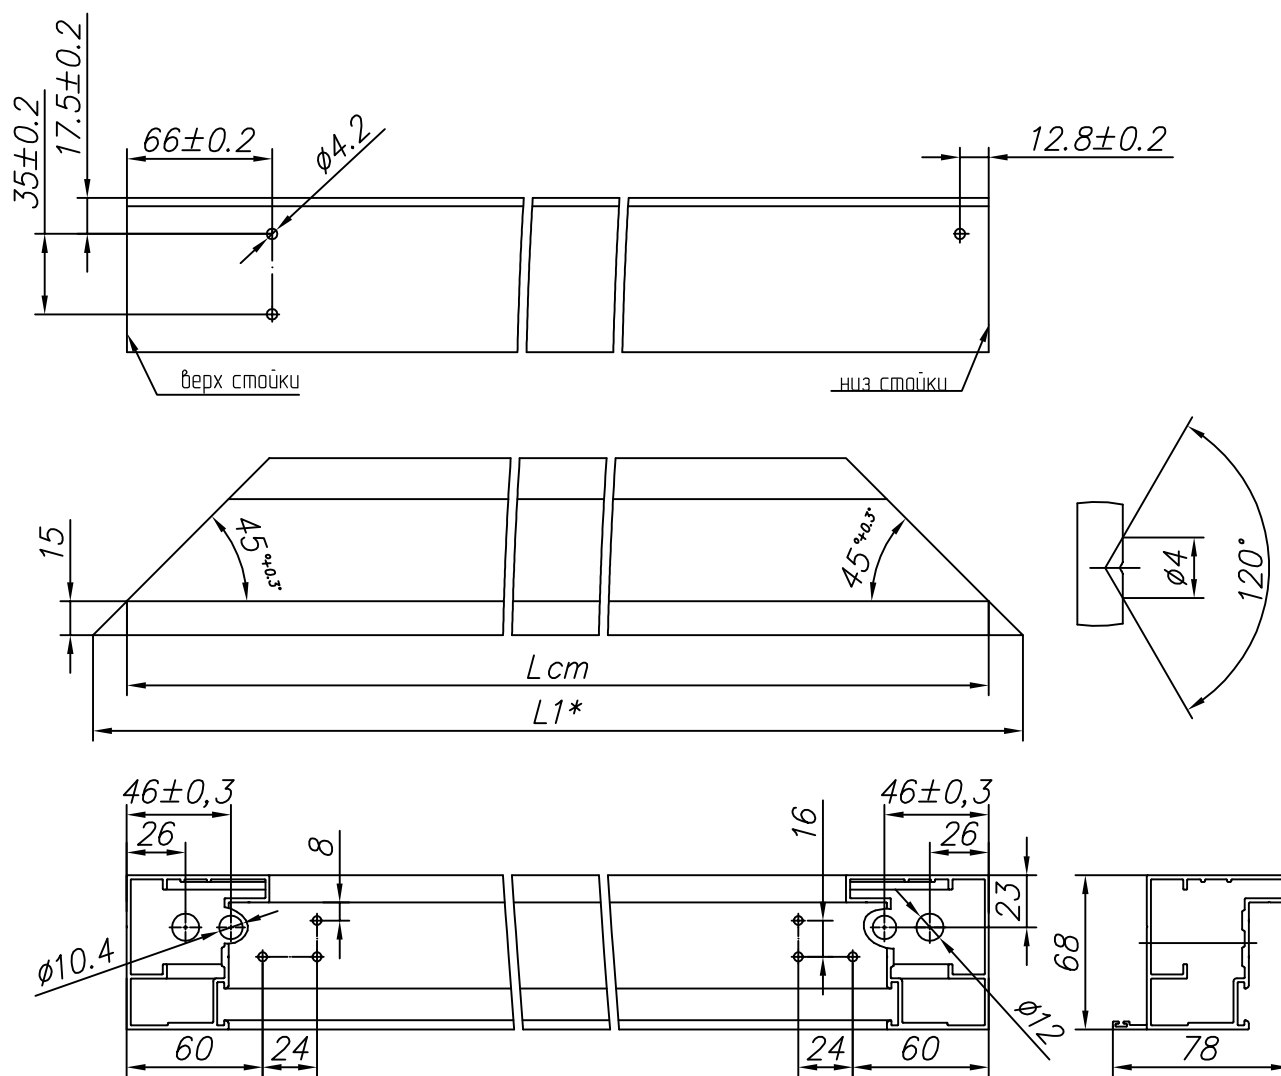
Изготовление стойки из профиля FLGU.400.0110 (стойка левая, открывание калитки внутрь)
